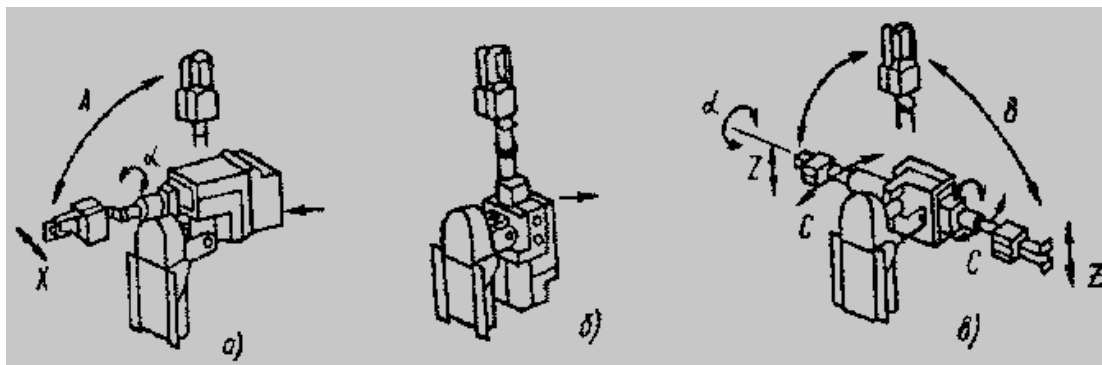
Координаты перемещения захвата робота мод М10П62.01: а – движение руки вперед и вниз; б – центральное положение; в-движение руки вниз и в сторону
